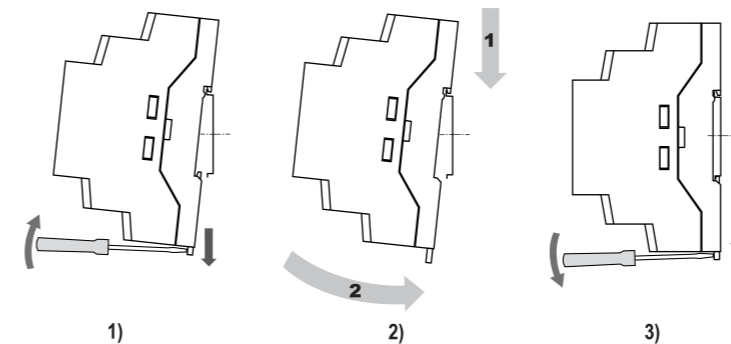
Монтаж прибора с креплением на DIN-рейку
